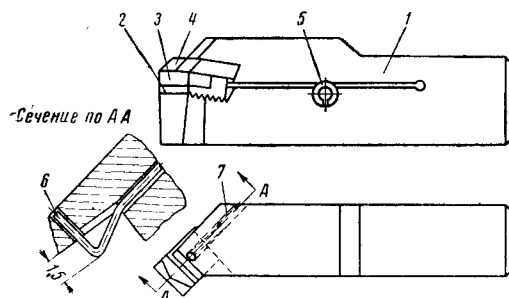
Упор резца конструкции С. Т. Полякова (деталь 3)
